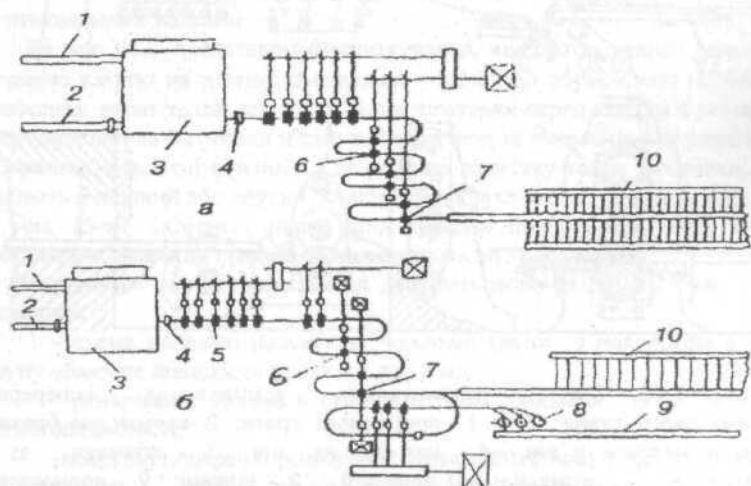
Напівнеперервний дрібносортний стан з однією (а) і дрібносортно-дротяний стан з двома неперервними групами клітей (б) : 1-уштовхувач заготовок;2-виштовхувач заготовок; 3-нагрівальна піч; 4-витягувач заготовок; 5-безперервна чорнова група клітей; 6 - лінійна група клітей; 7-чистові кліті (на стані «б» з триклітьовою неперервною групою); 8 - моталки дроту; 9-конвейер бунтів дроту; 10-холодильник
